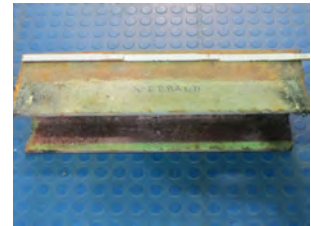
Verbandsstab, Grundwerkstoff G02, Foto: SLV Halle GmbH
